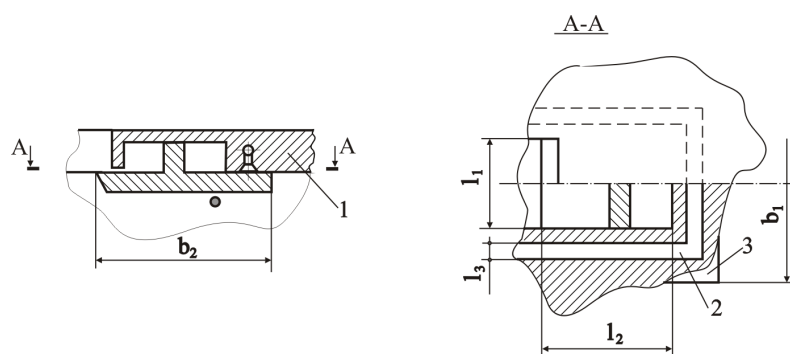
Схема расположения кармана и отверстий для газовой смазки.
